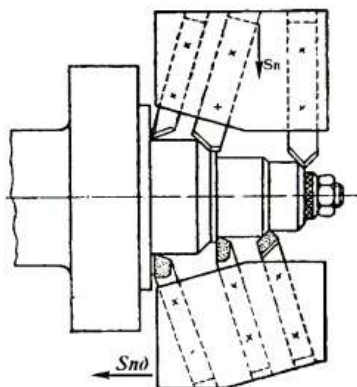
Схема обробки заготовки на одношпиндельному токарно багаторізцевому напівавтоматі
